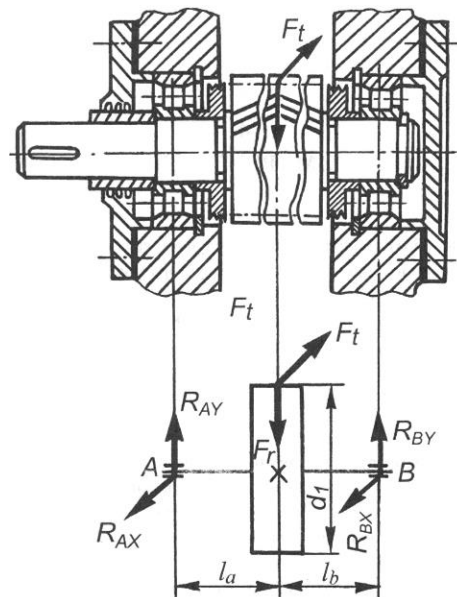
Подшипниковые узлы ведущего вала шевронного редуктора
